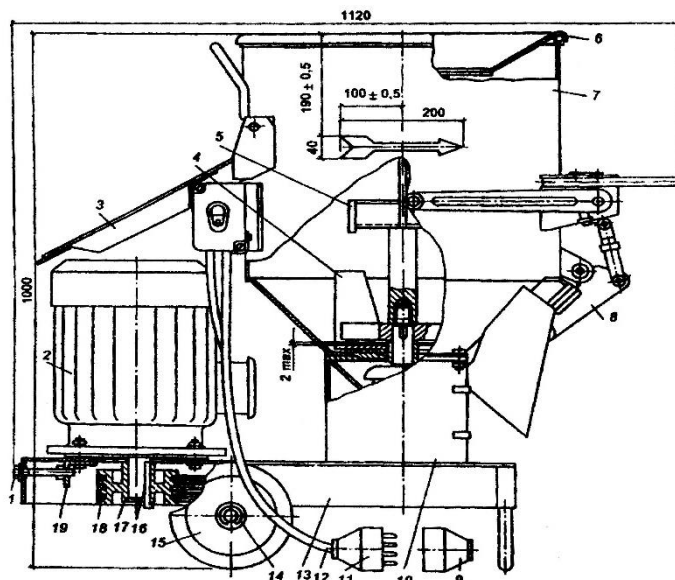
Бетоносмеситель турбулентный принудительного перемешивания: 1 – натяжной болт; 2 – электродвигатель; 3 – щиток; 4 – ротор; 5 – лопасть; 6 – крышка; 7 – бак; 8 – разгрузочное устройство; 9 – розетка; 10 – ограждение; 11 – вилка; 12 – кабель; 13 – основание с приводным валом; 14 – стопорное кольцо; 15 – колесо; 16 – вал электродвигателя; 17 – шкив; 18 – ремень; 19 – салазки
